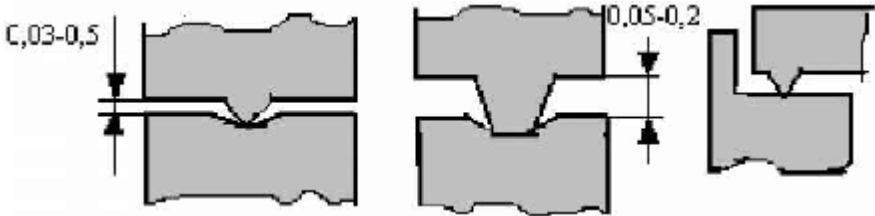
Підготовка кромок для передаточного зварювання
